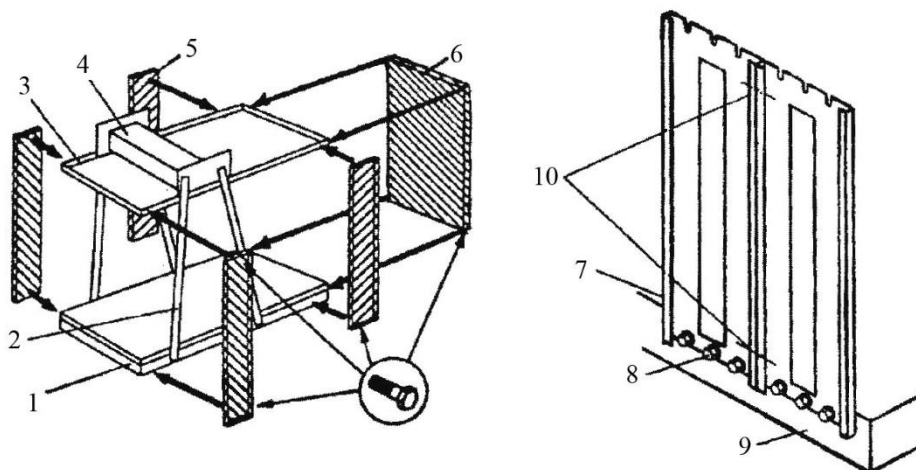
Схема конструкции и сборки купе кабины модульного типа:
